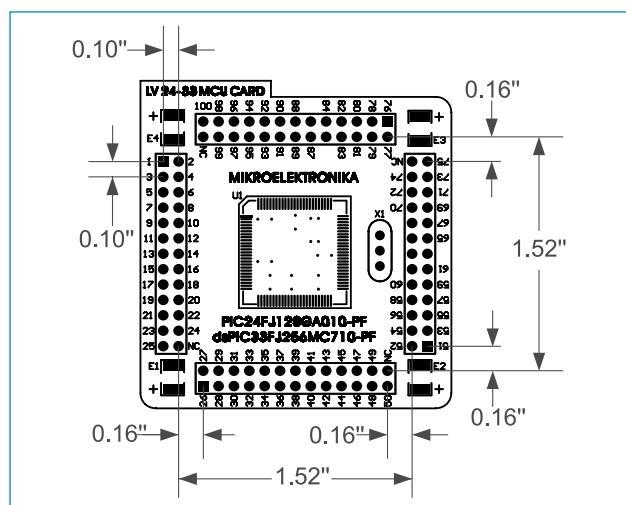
Dimensiones de la tarjeta MCU para las *MCU Card 1* a *MCU Card 8
